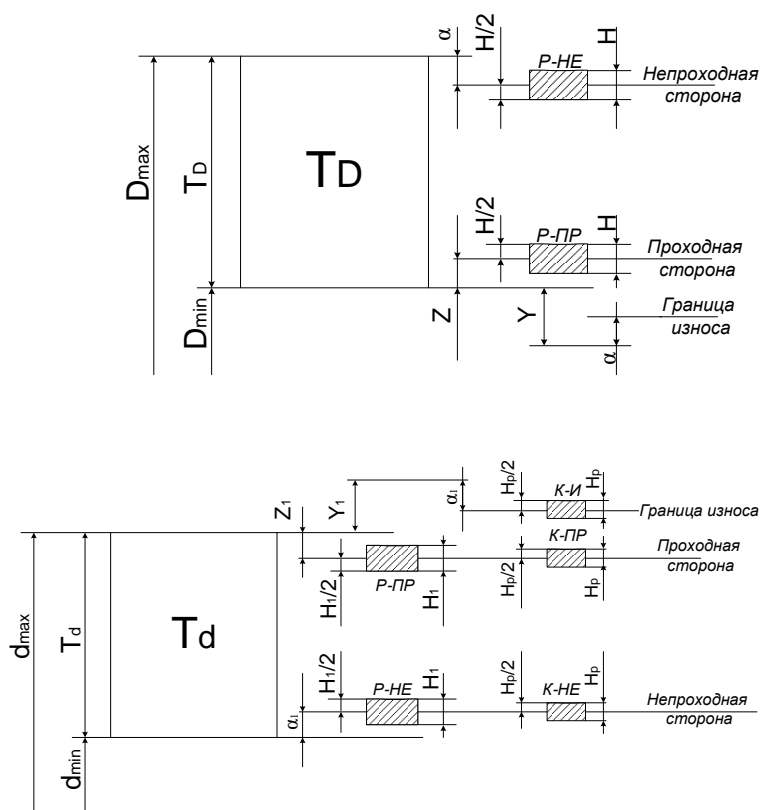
Схемы расположения полей допусков калибров
